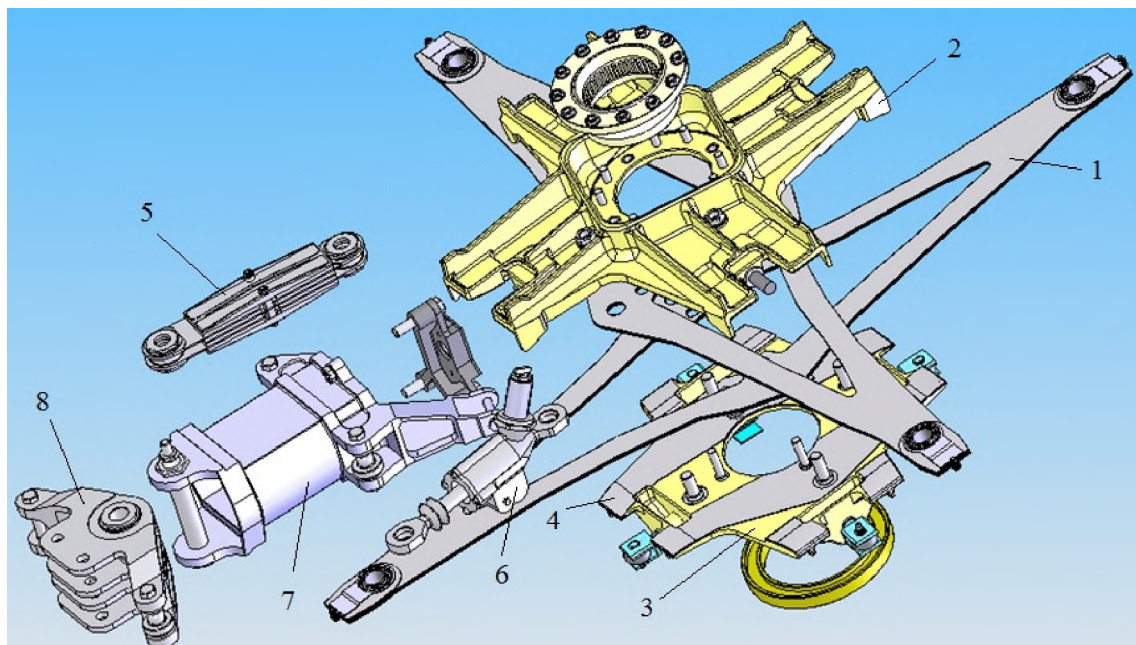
Конструкция втулки НВ с пластинчатым торсионом вертолета Ми-34 [18]:
